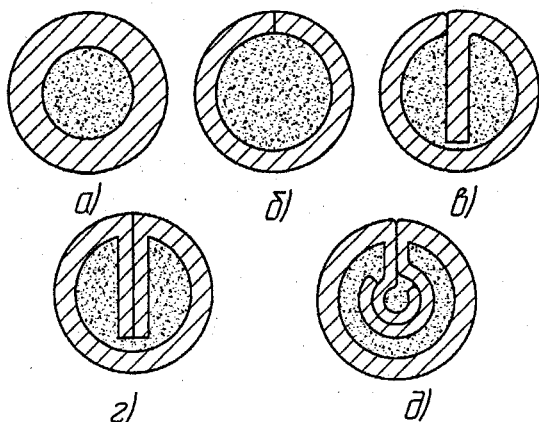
Поперечний переріз порошкових дротів: а, б — трубчастий; в — однозагинний; г — двозагинний; д — двошаровий
